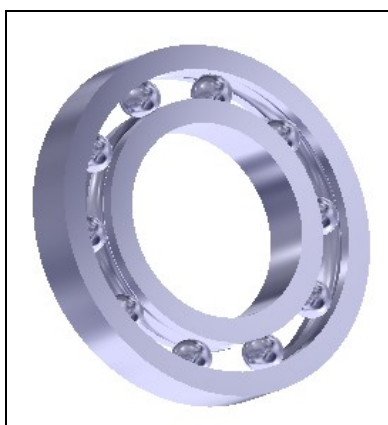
Rodamiento turbocompresor, pieza
